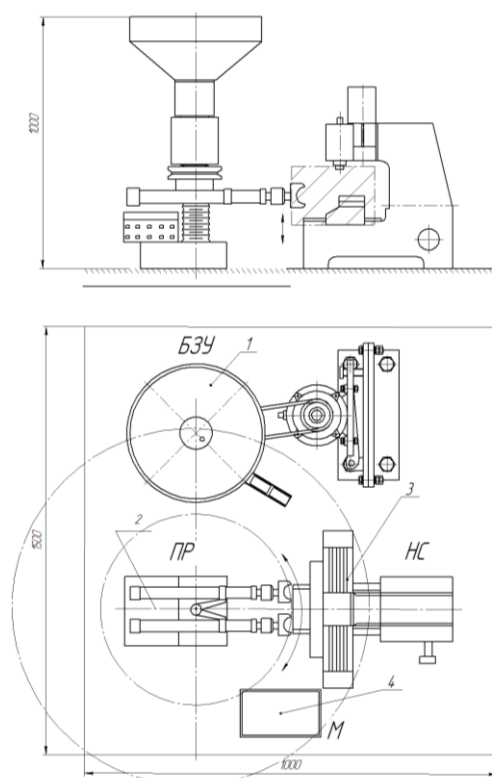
Вариант компоновки РТК (планировка). Структура РТК: ПУ – пульт управления; ПР – промышленный робот; НС – настольно сверлильно-фрезерный станок; М – магазин деталей ;БЗУ – бункерно-загрузочное устройство.
